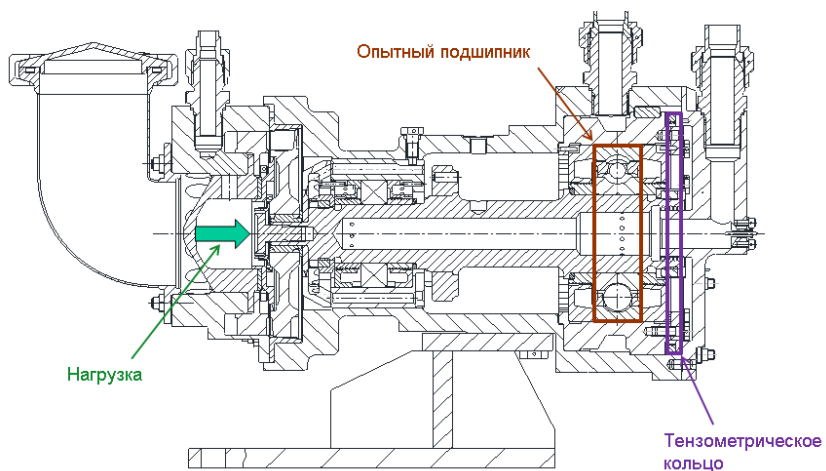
Опора с подшипником, смазываемым консистентной смазкой
